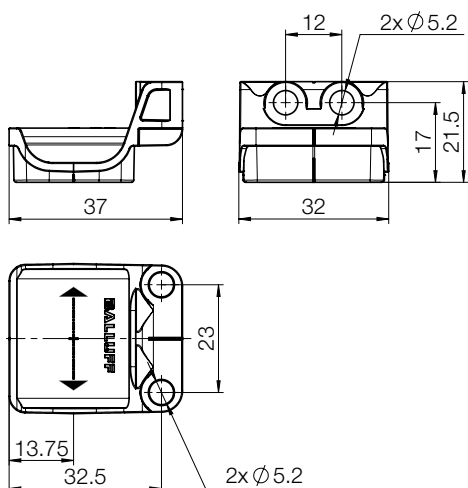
Misure di montaggio trasduttore di posizione BAM TG-IR-036-B, la freccia indica la direzione di movimento (per il montaggio vedere Fig. 5-4)
